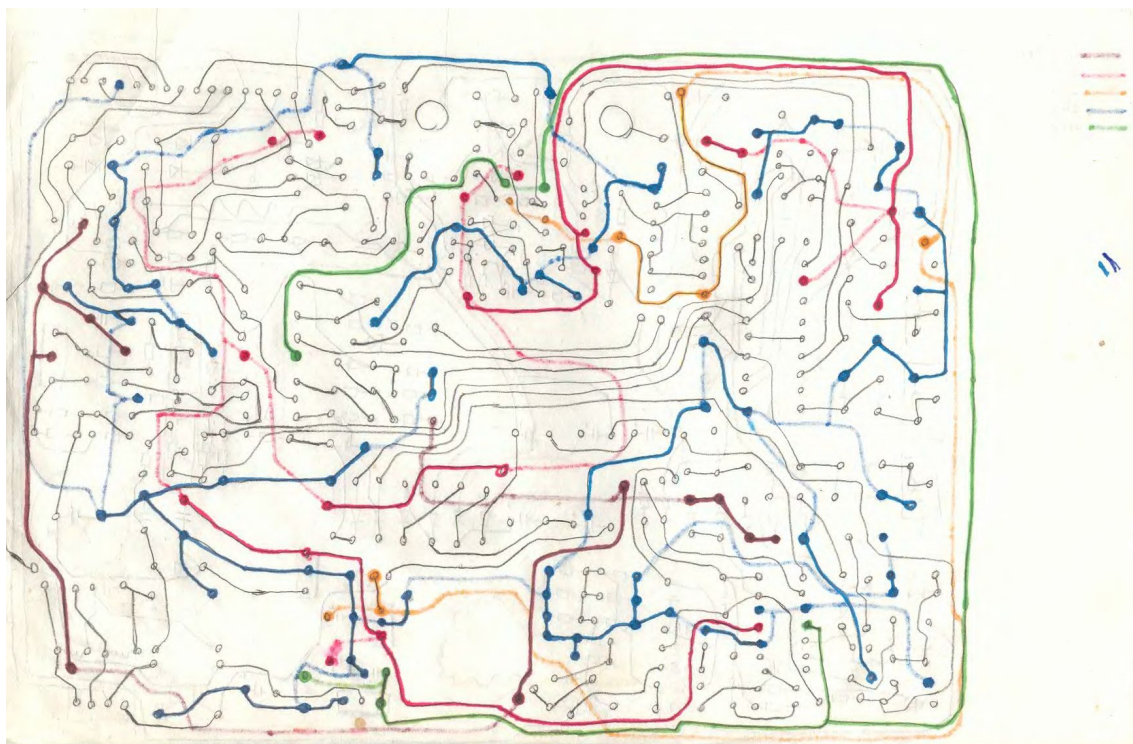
Зарисовка платы управления сварочного источника RytmArc со стороны паек.
